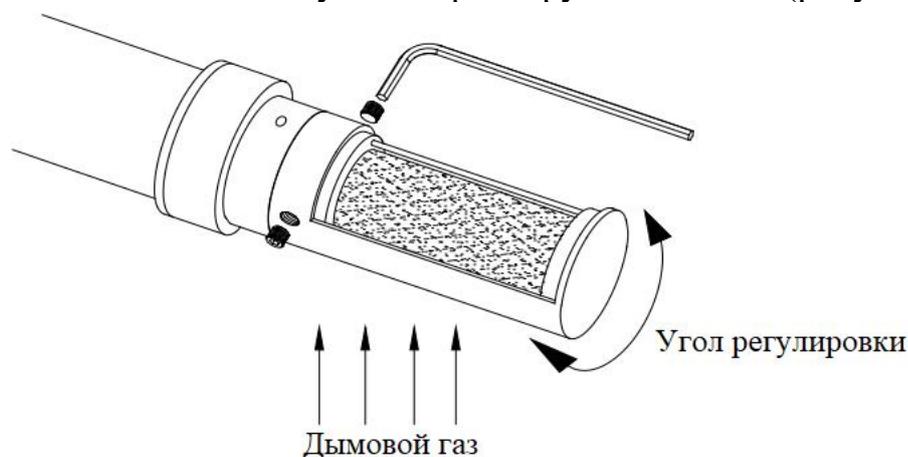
Регулировка кожуха крышки фильтра
